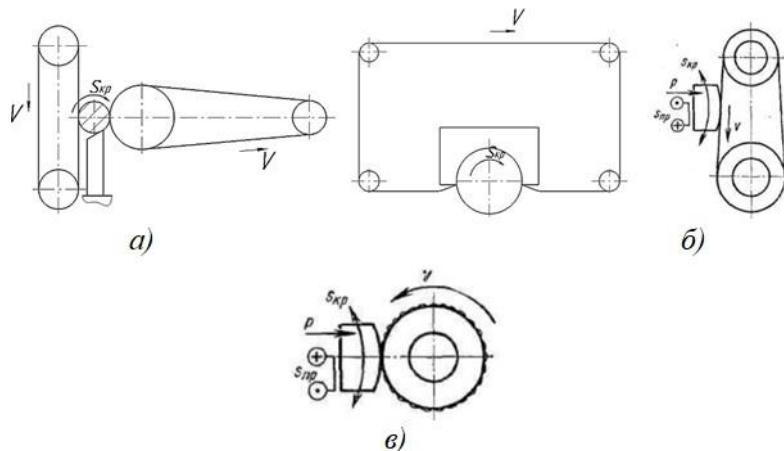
Схема притирання зовнішньої циліндричної поверхні
